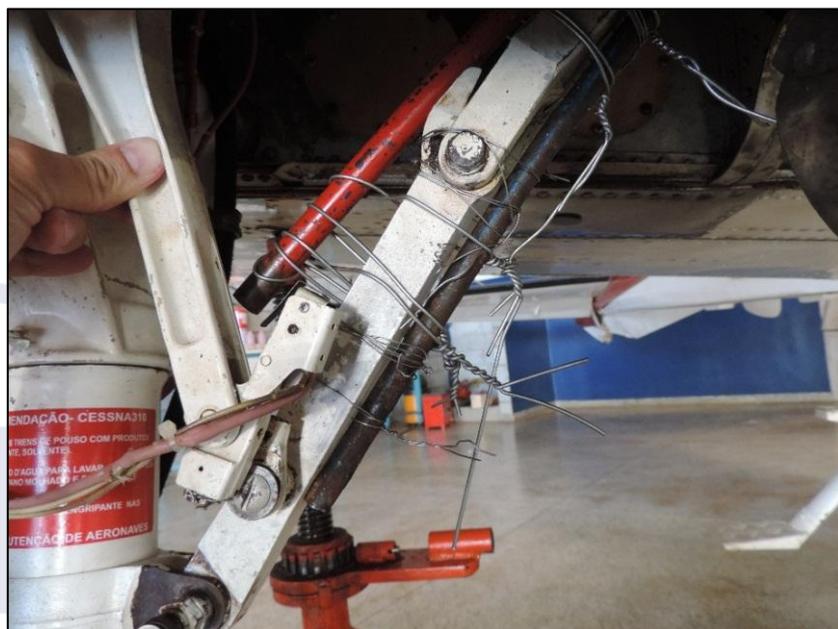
Parte superior do trem de pouso principal direito quebrada.
